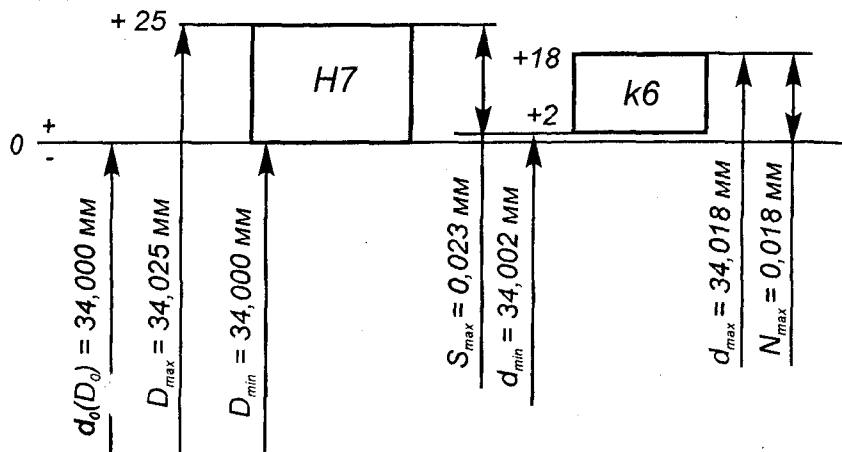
Схема расположения полей допусков сопрягаемых деталей
